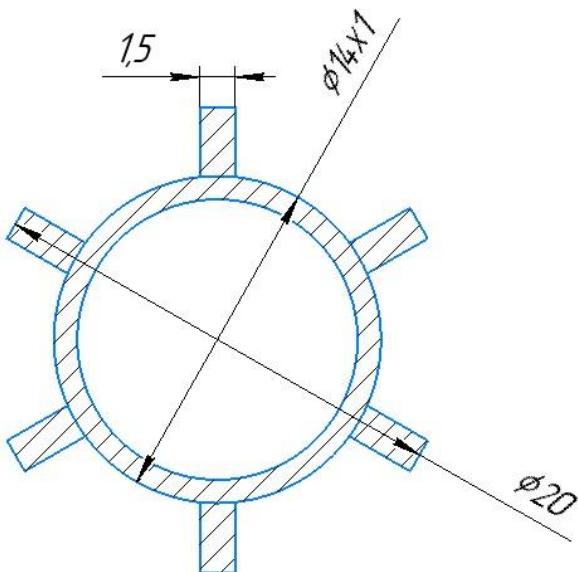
трубка с продольным оребрением наружной поверхности
